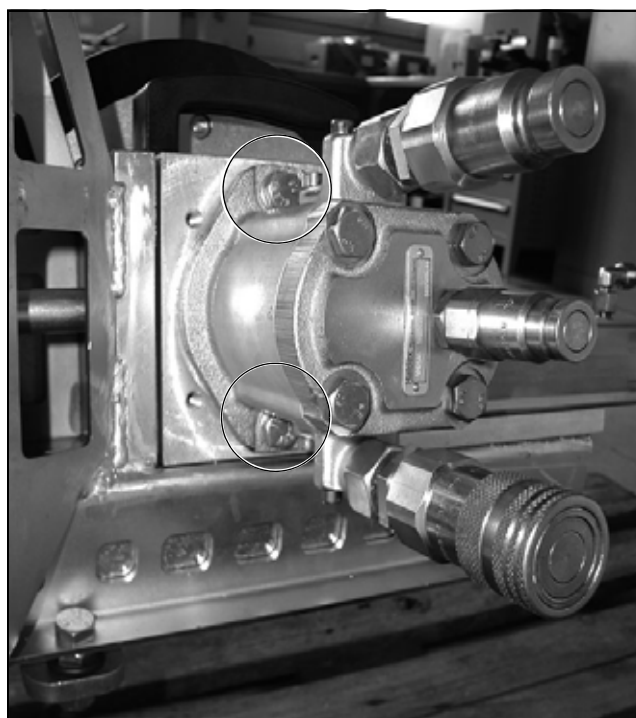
Монтаж (поставленного) гидродвигателя привода (HM)
